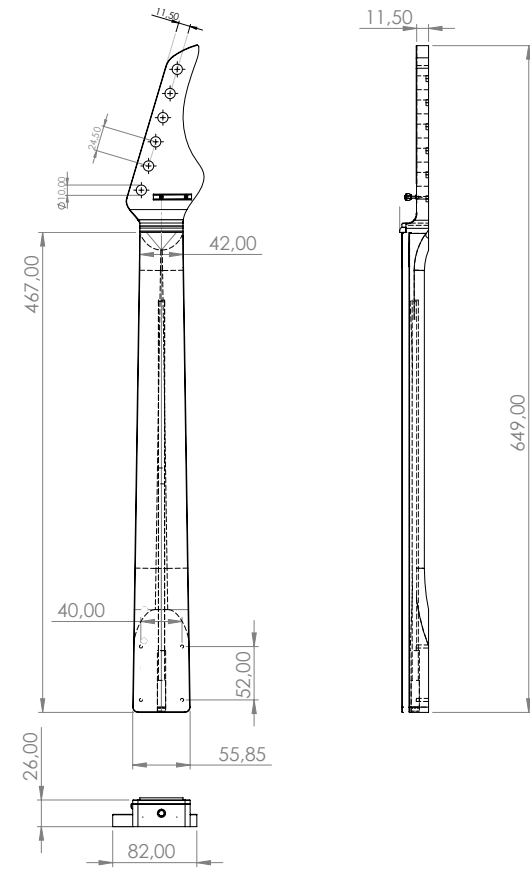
Desenho técnico - Protótipo “Braço Aço”.
